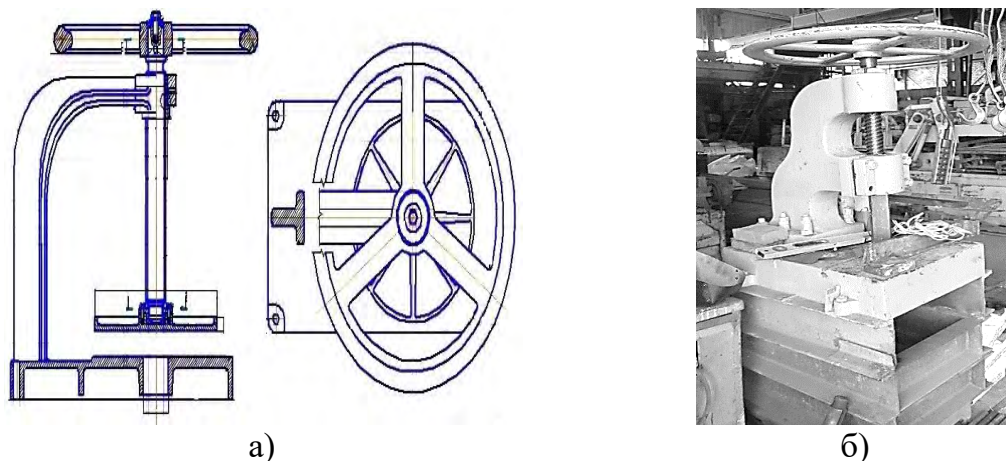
Ручной пресс: а) сборочный чертеж; б) оригинальный механизм.
